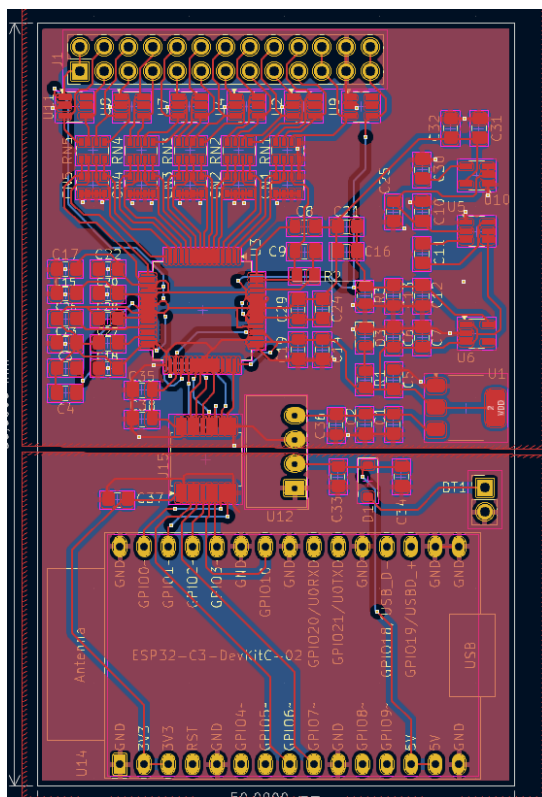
Diseño Layout de la PCB, con planos de masa
